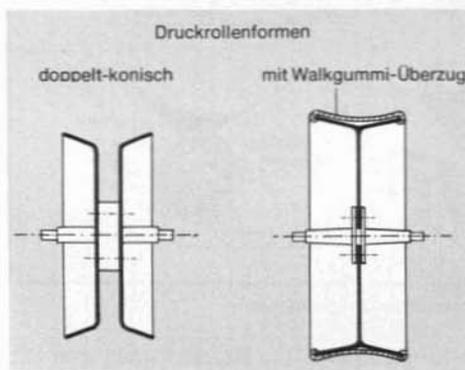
Druckrollenformen bei Einzelkornsämaschinen
